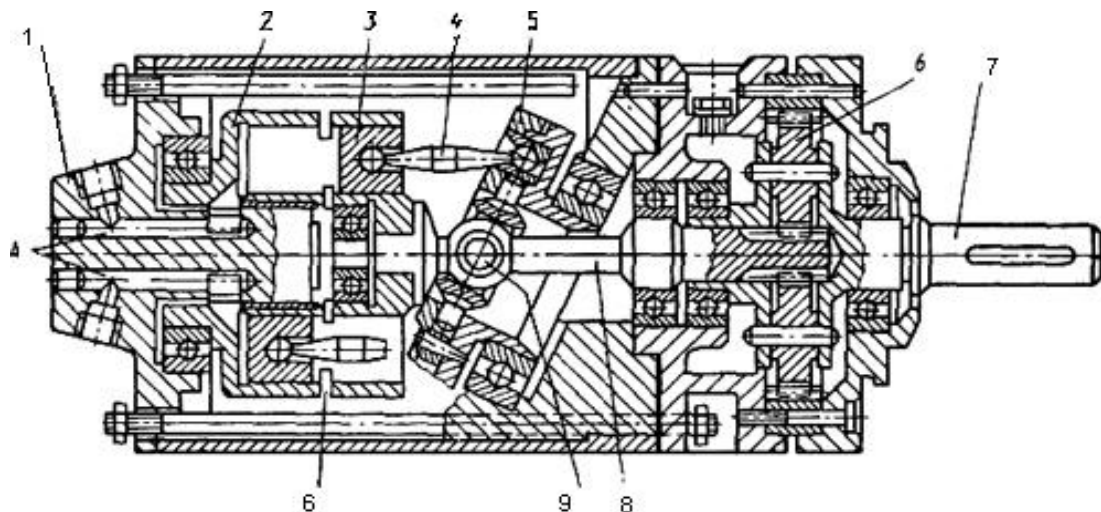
Аксиально-поршневой мотор с одноступенчатым редуктором
